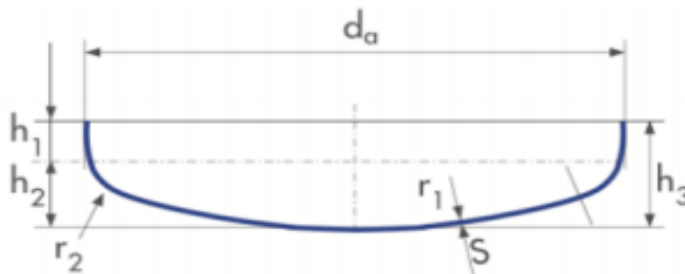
Muestra geometría de los cabezales y fondos
